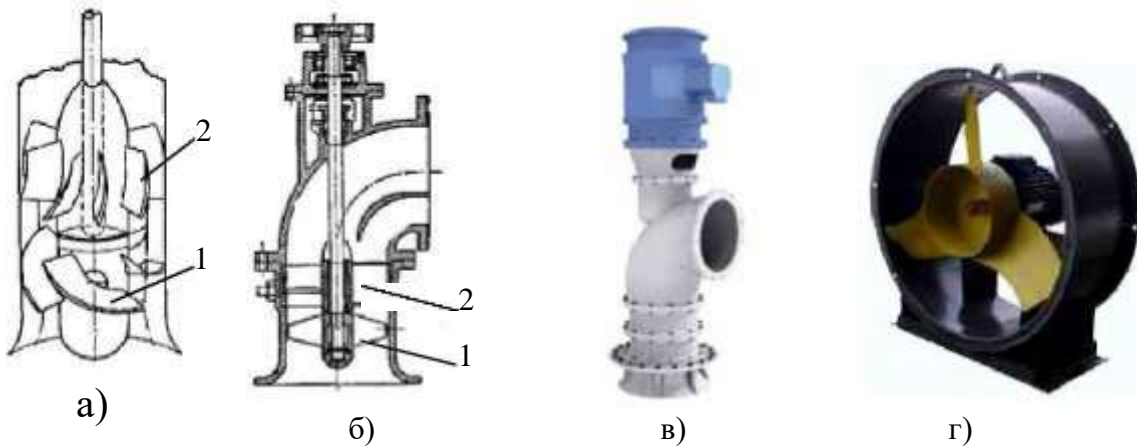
Конструкція (а, б) та зовнішній вигляд осьового насоса (в) та вентилятора (г): 1 – робоче колесо; 2 – напрямний апарат
